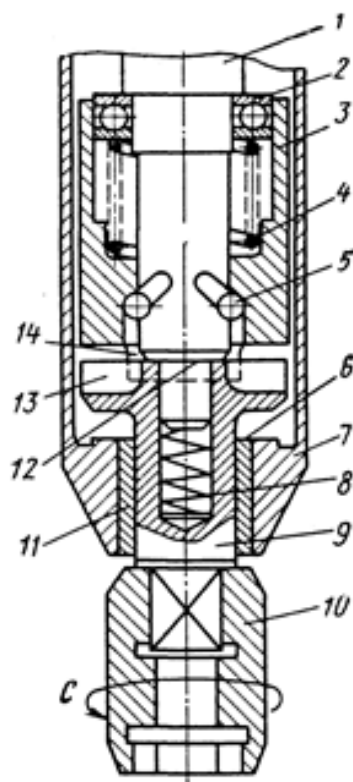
Ударный механизм с винтовым перемещением бойка:
